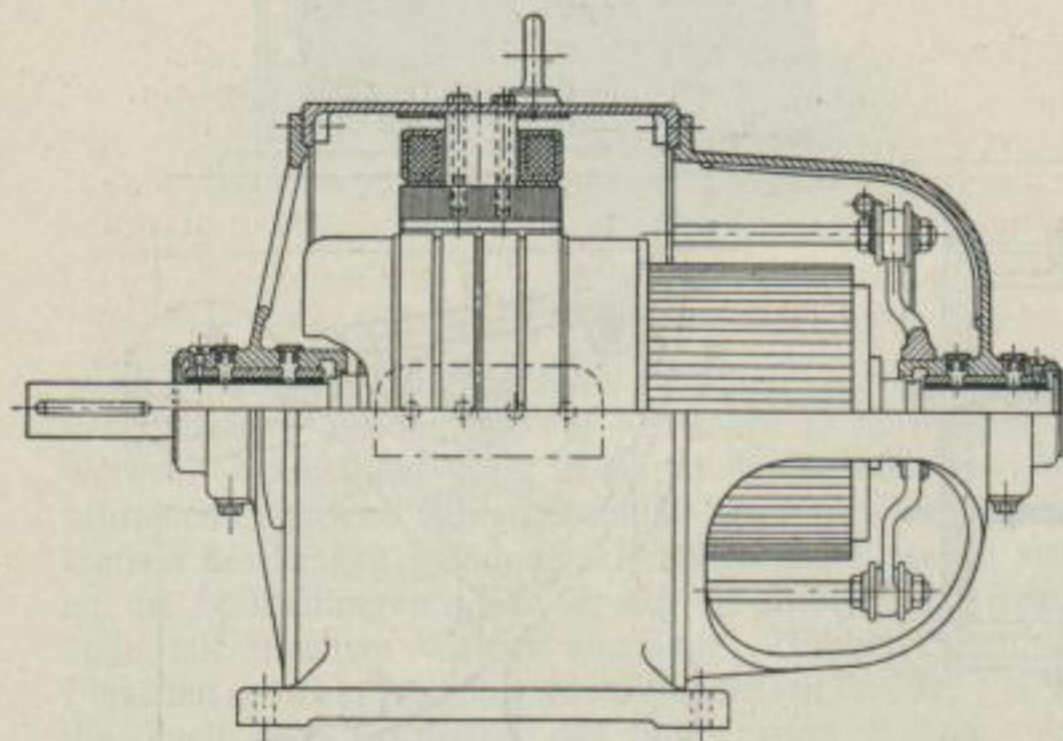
REG-Schweißdynamo, 30 KW, 720 Umdr./Min.
